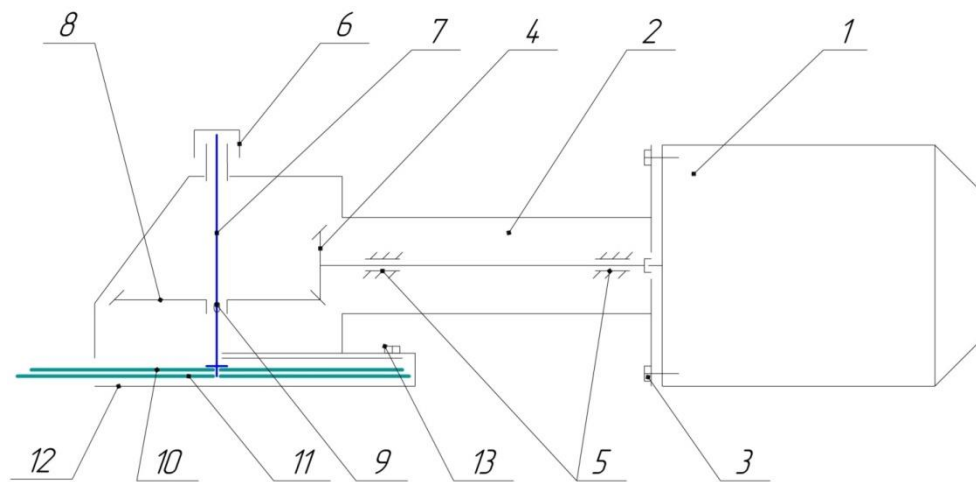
Принципова схема стригальної машинки ротаційного типу: 1 – електродвигун, 2 – корпус, 3 – гвинти, 4 – конічний валшестерня, 5 – підшипники, 6 – притискна головка, 7 – вісь, 8 – конічне колесо, 9 – шпонка, 10 – дисковий ніж, 11 – гребінка, 12 – притискна пластина, 13 – гвинти.
